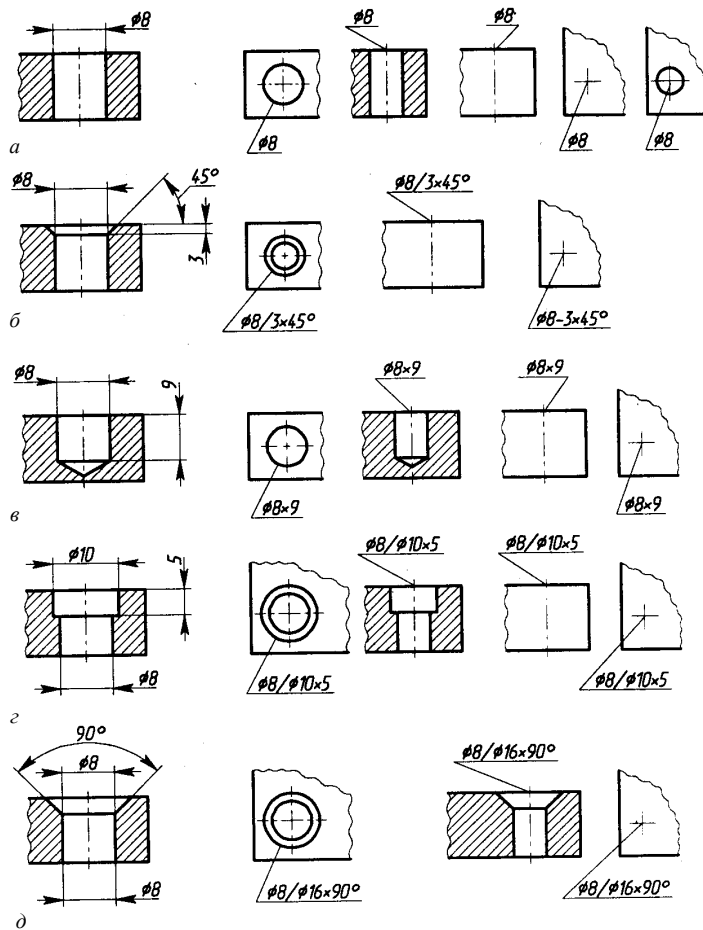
Варианты простановки размеров диаметра и глубины отверстий:
